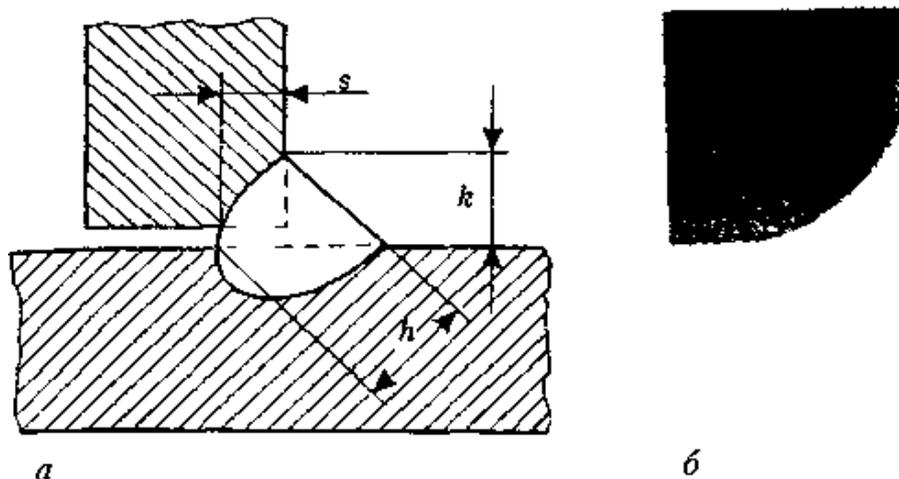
Сварка углового шва без разделки кромок:
